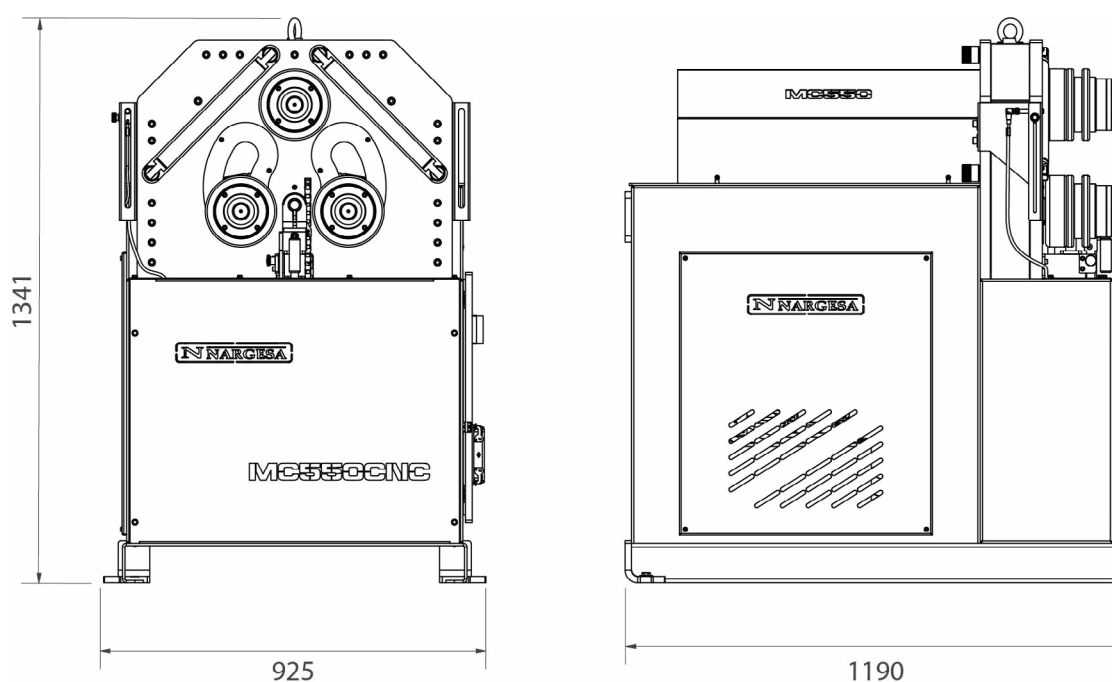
Dimensions extérieures de la cintreuse MC550CNC
